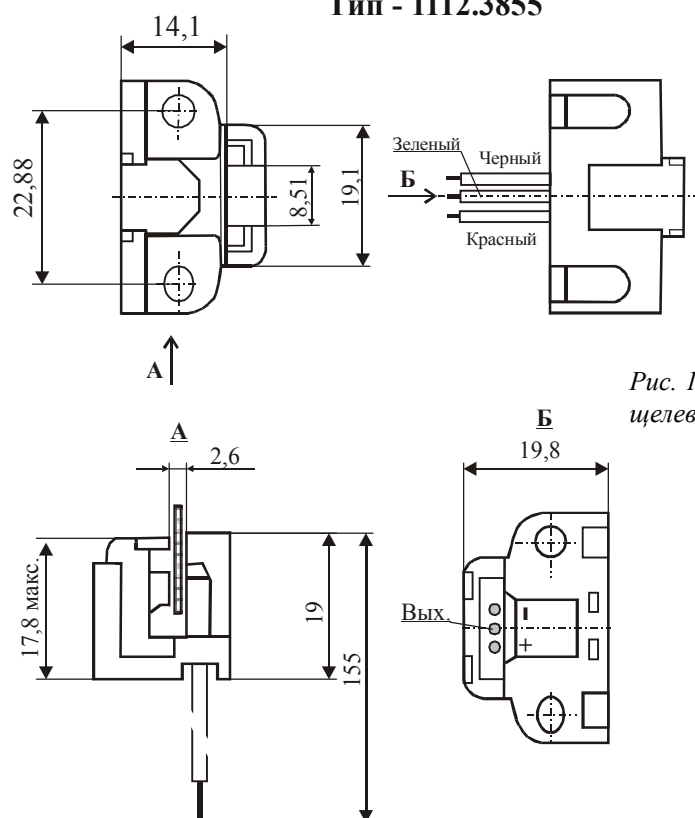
Внешний вид и габаритные размеры целевого датчика типа 1112.3855
